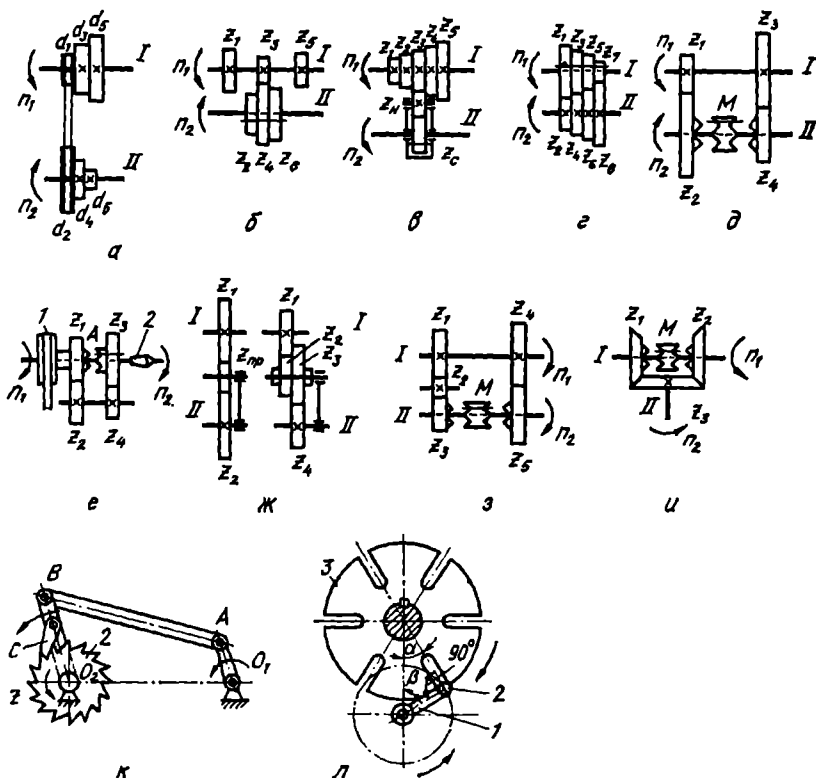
Механизмы ступенчатого регулирования металлорежущих станков
